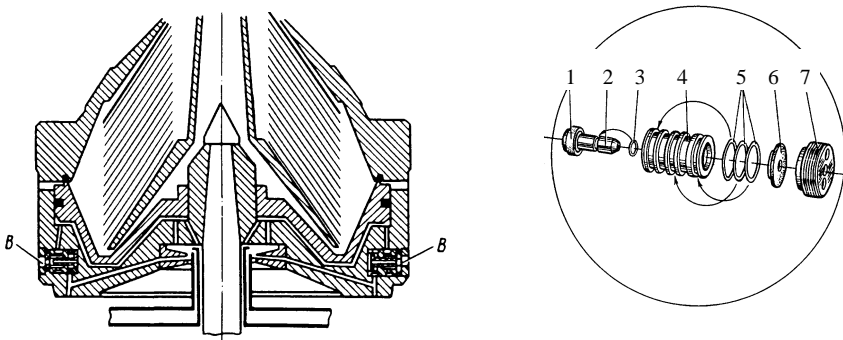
Клапан сепаратора: 1 – поршень; 2 – шток; 3 – кільце гумове; 4 – корпус; 5 – кільця фторопластові; 6 – кришка; 7 – гайка
